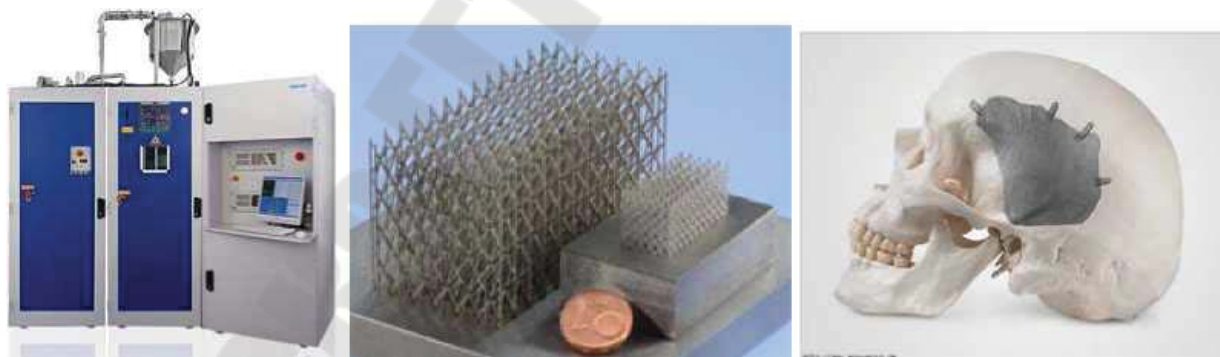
АФ машина Realiser SLM 250 и образцы изделий из титана
